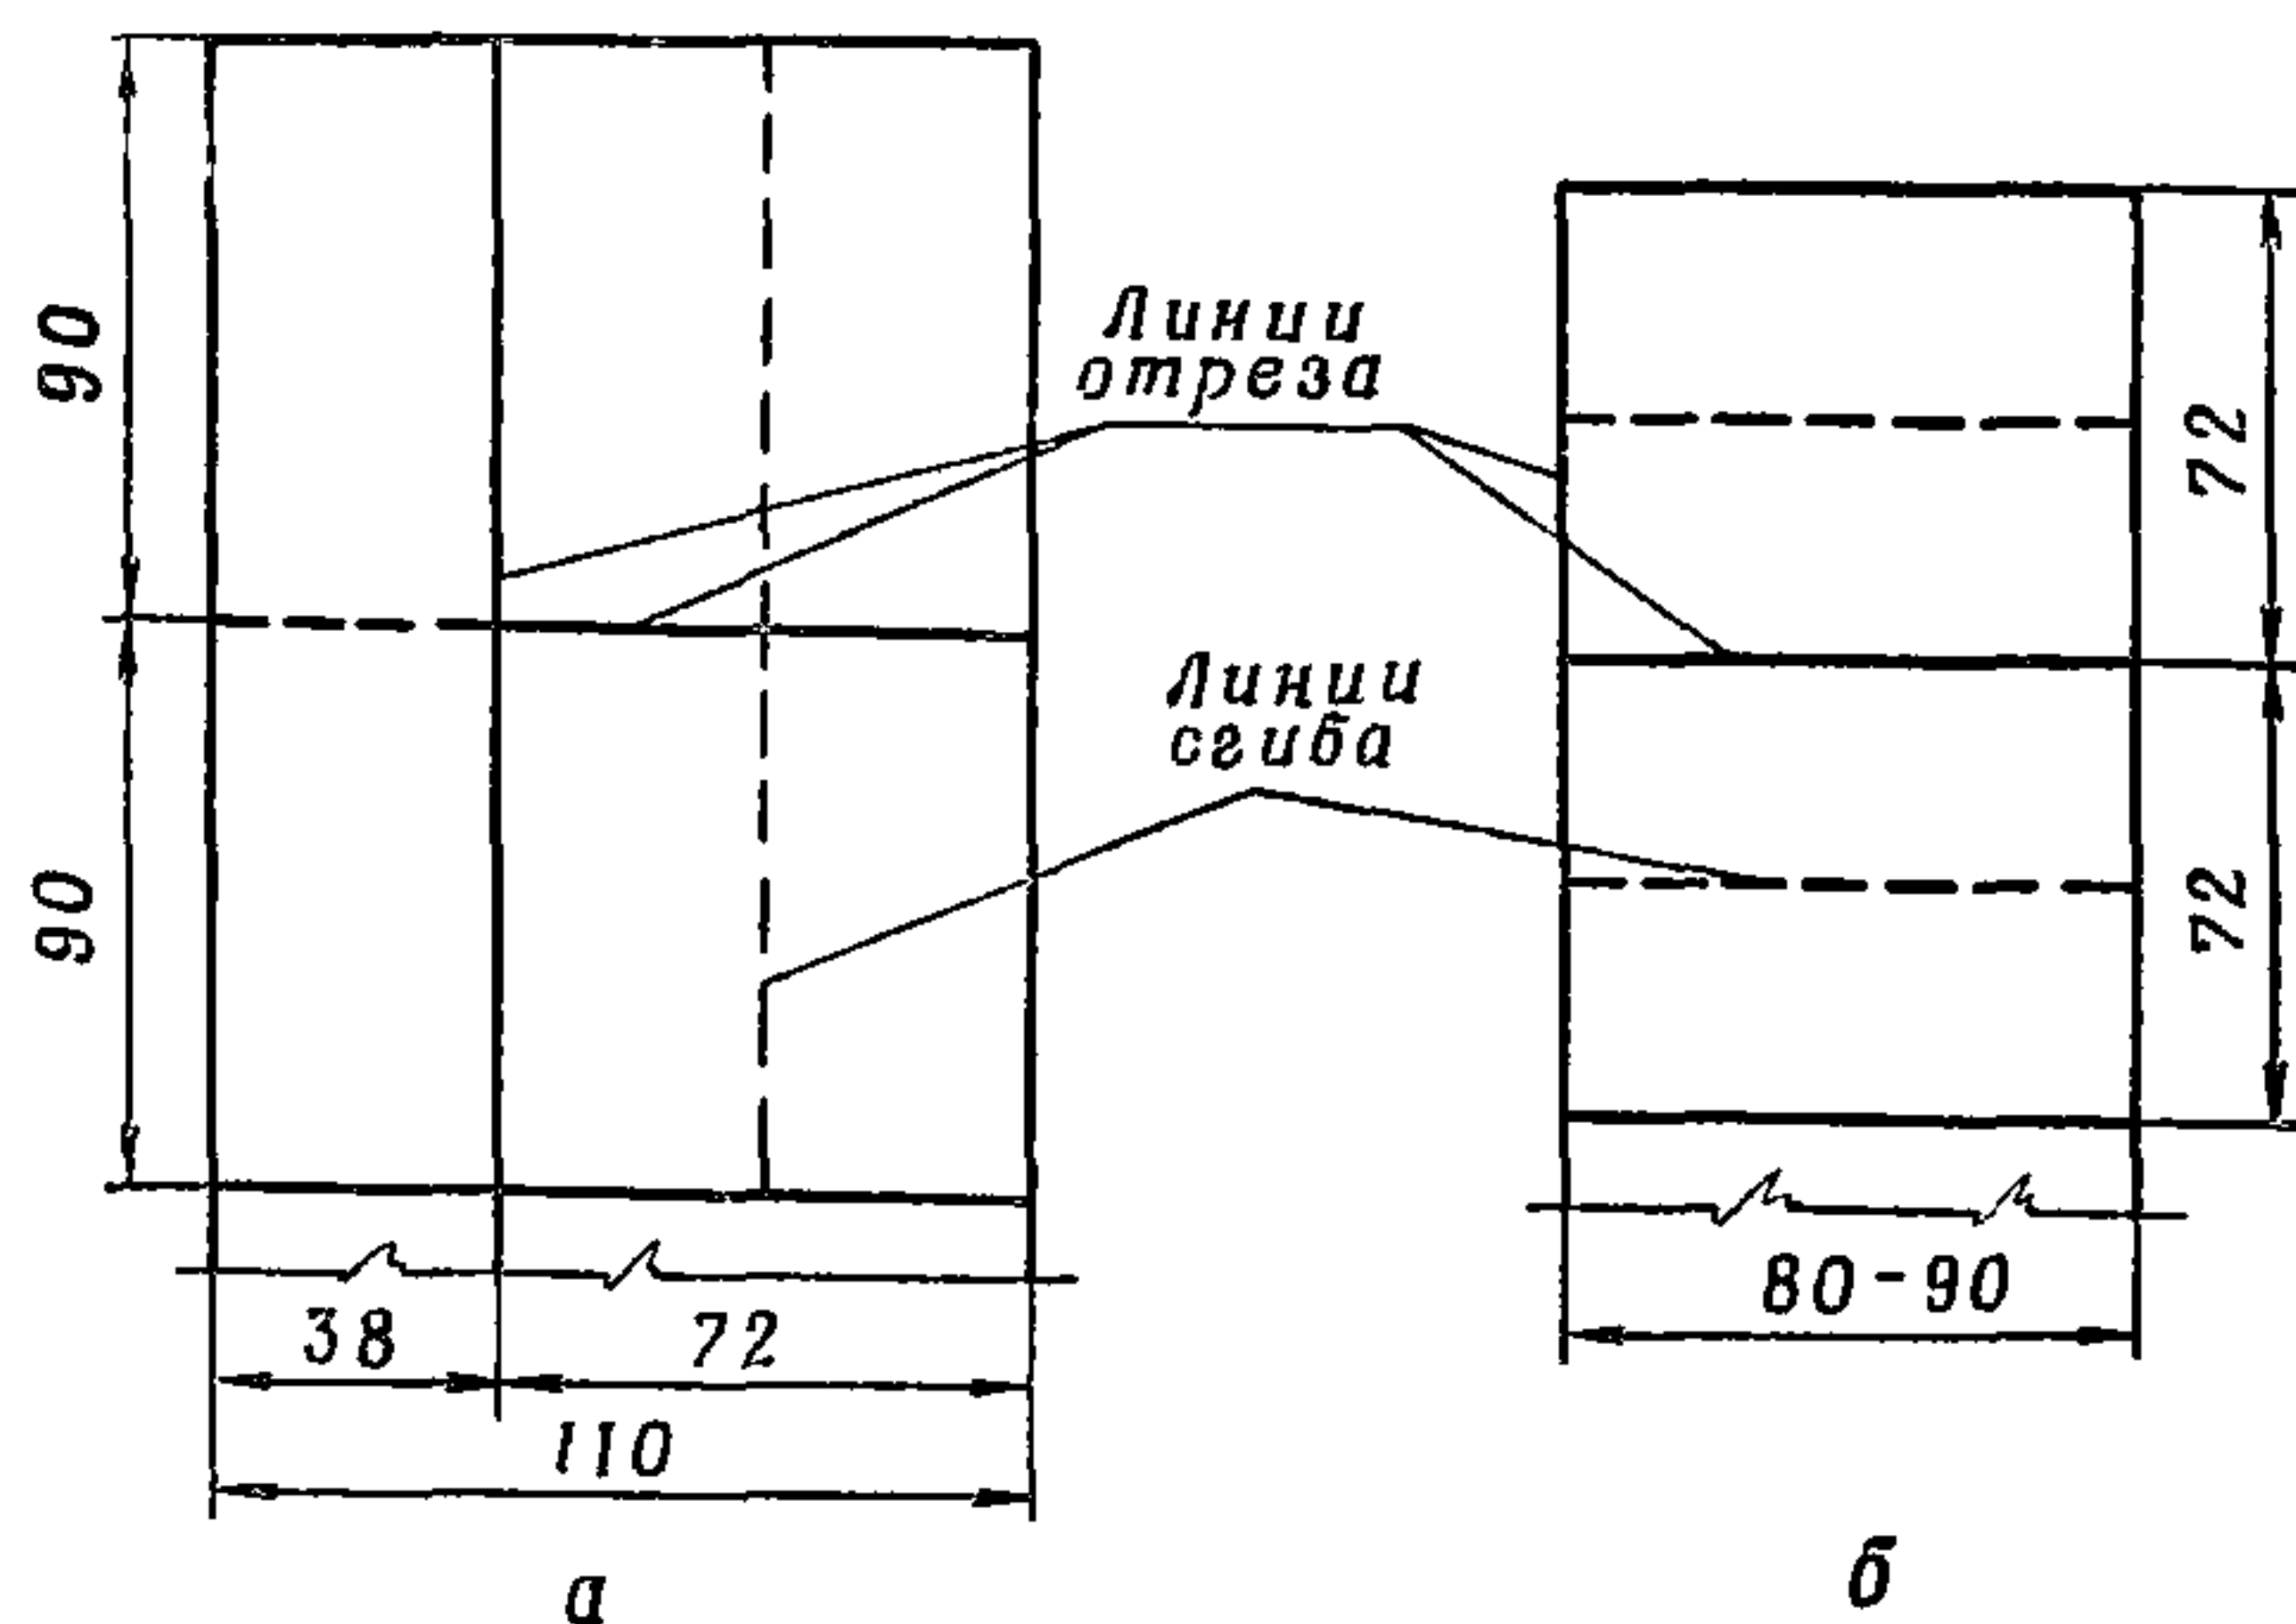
Схема раскроя ткани для пошивки грунтонабивных мешков:
